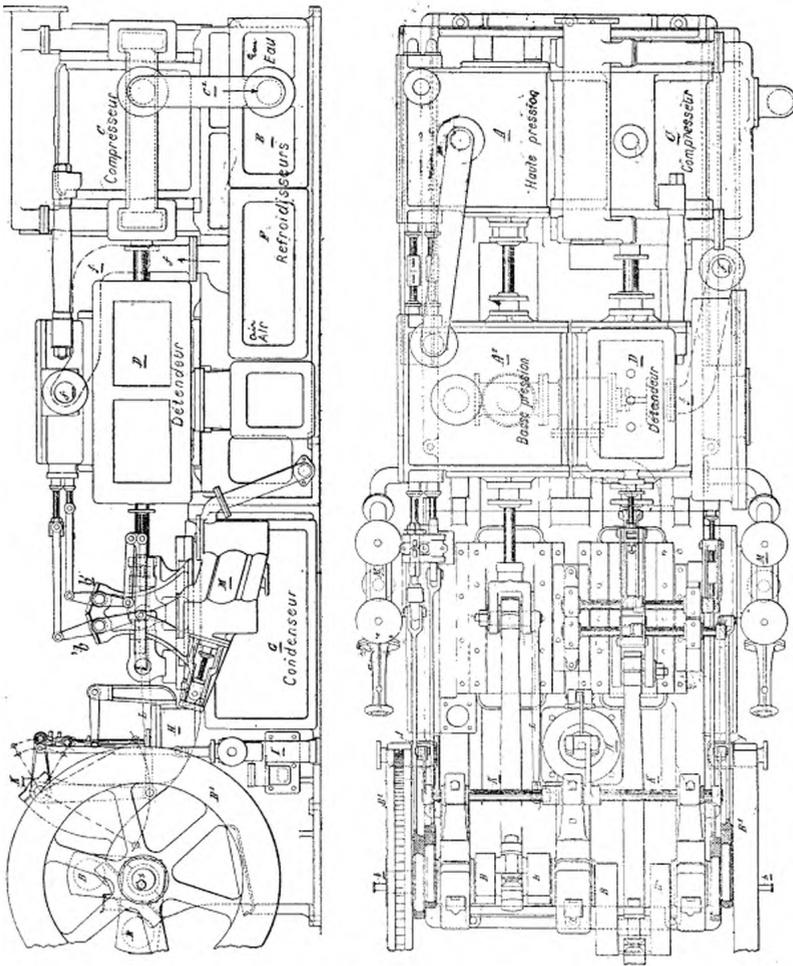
et 70. — Haslam. Machine horizontale à moteur compound
